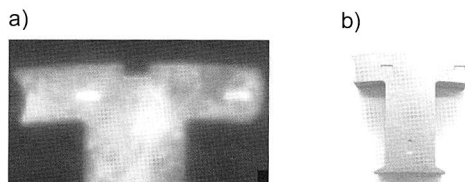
Stanzpaketierter Statorzahn; a) Wärmebildaufnahme, b) unpräpariertes Blechpaket
